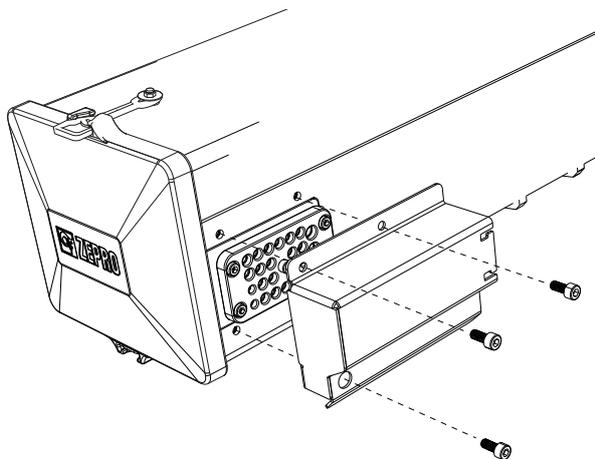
La cubierta de protección del prensaestopas está montada con tres tornillos
